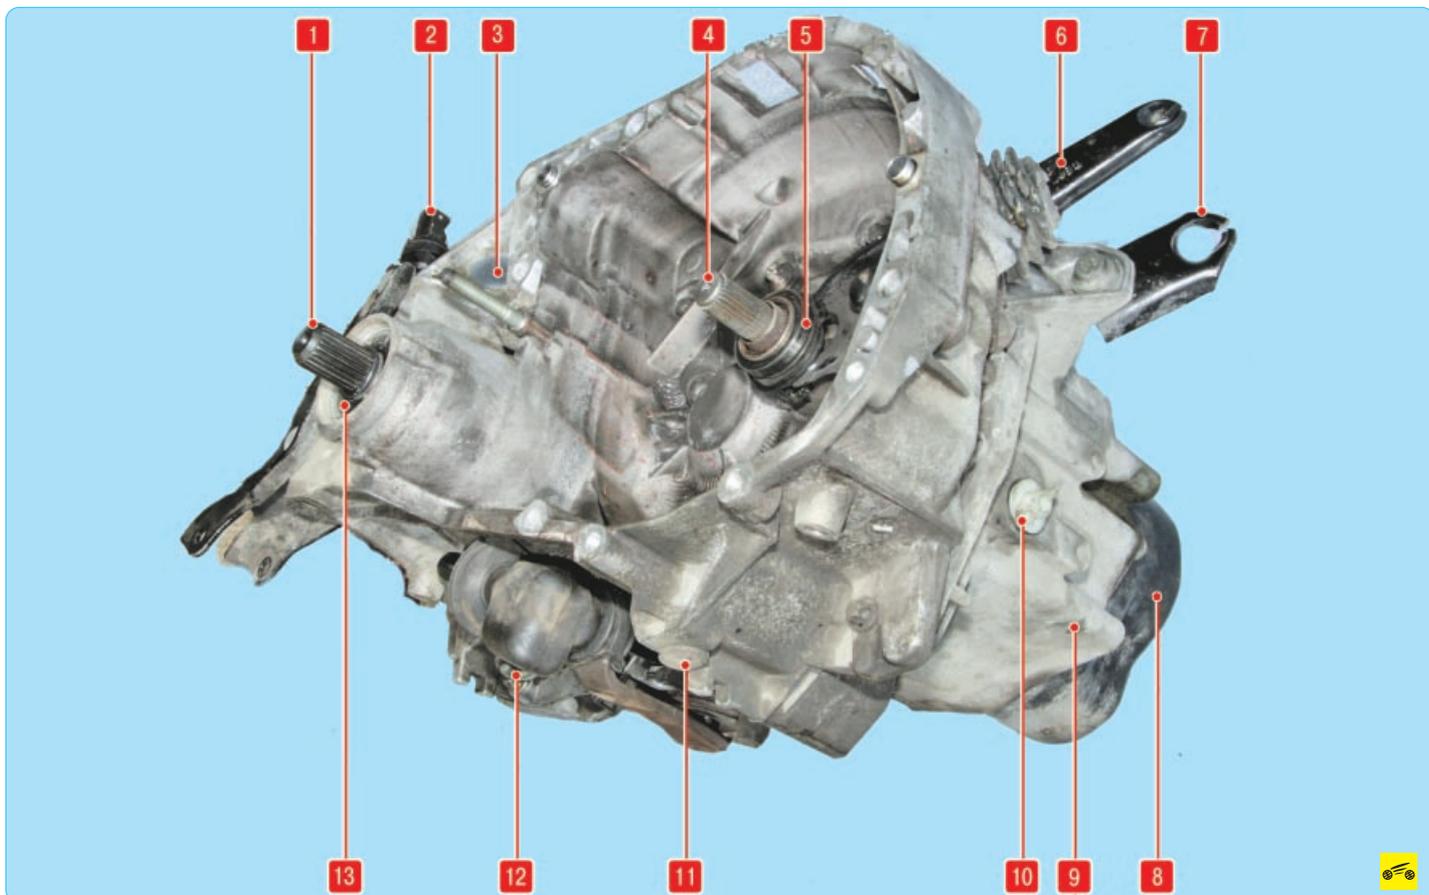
Механическая коробка передач: 1 – хвостовик полуосевой шестерни; 2 – датчик скорости; 3 – картер сцепления; 4 – первичный вал; 5 – подшипник выключения сцепления; 6 – вилка выключения сцепления; 7 – упор оболочки троса привода выключения сцепления; 8 – задняя крышка; 9 – картер коробки передач; 10 – пробка маслосливного отверстия; 11 – пробка масляного отверстия; 12 – механизм переключения передач; 13 – сальник хвостовика правой полуосевой шестерни дифференциала
